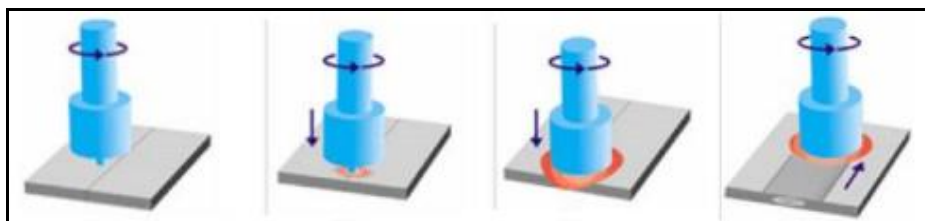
Etapas iniciais da soldagem FSW. Fonte: Rodriguez et al, 2013 p.4.
